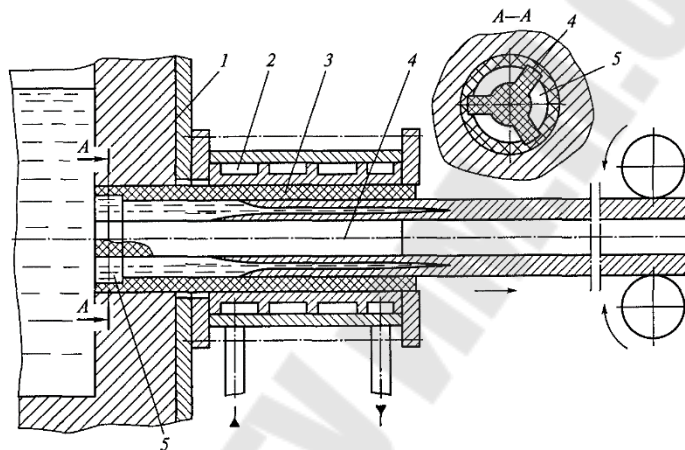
Схема кристаллизатора для горизонтального непрерывного литья трубчатых заготовок и профилей: 1 – раздаточная печь; 2 – водоохлаждаемая рубашка; 3 – графитовый вкладыш; 4 – стержень; 5 – отверстие для подвода расплава
